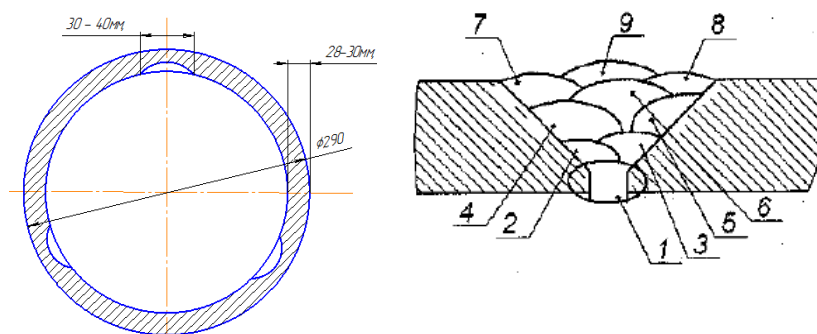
Схема расположения прихваток и раскладки валиков многопроходного шва
